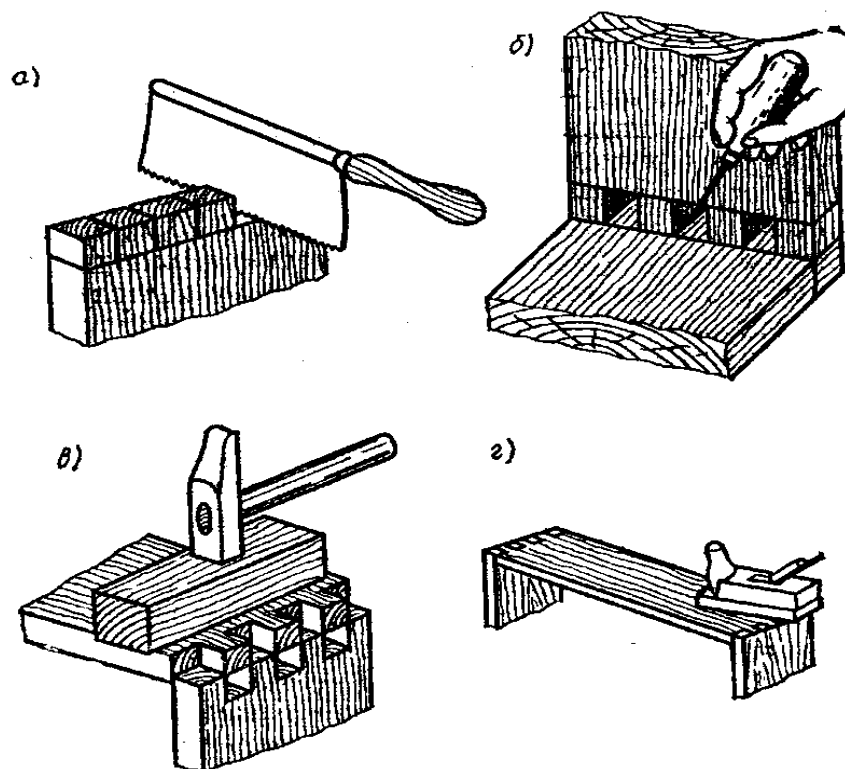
Ящикові кутові з'єднання з прямими наскрізними шипами: *а* - випилювання шипових пазів; *б* - розмітка шипів шилом; *в* - з'єднання шипа з пазом; *г* - обробка рубанком кутового з'єднання.
